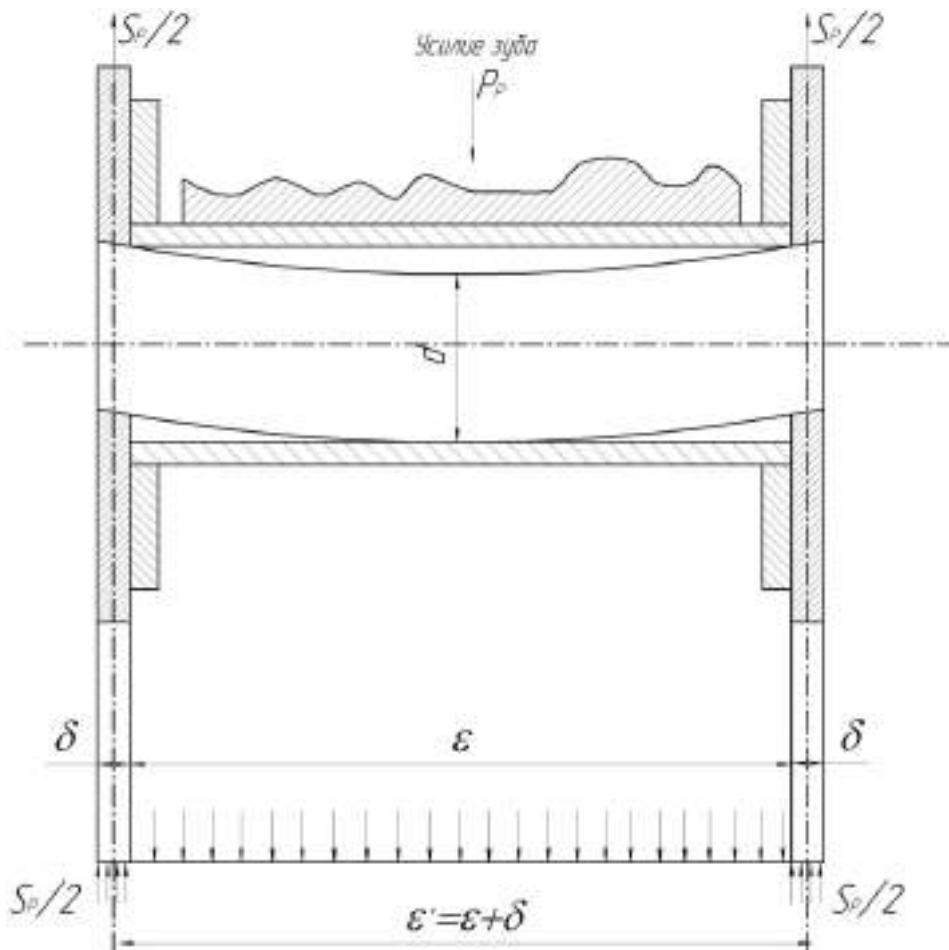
Розрахункова схема для перевірного розрахунку валика
